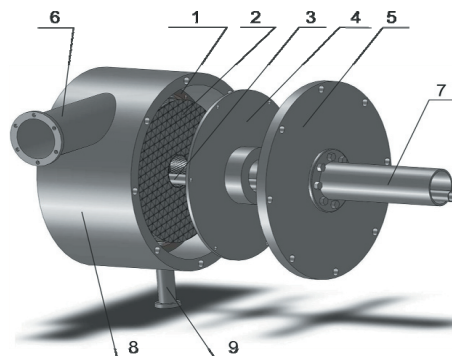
РМА з перфорованим ротором: 1 – ротор; 2 – контактний пристрій; 3 – патрубок подачі рідини; 4 – кришка ротора; 5 – кришка корпусу; 6 – патрубок подачі газу; 7 – патрубок виходу газу; 8 – корпус; 9 – патрубок відводу рідини
